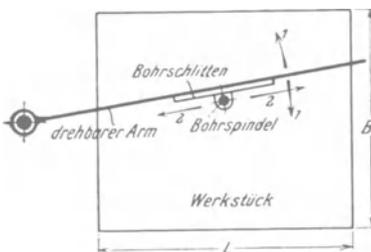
Einstellbarkeit der Auslegerbohrmaschine.
